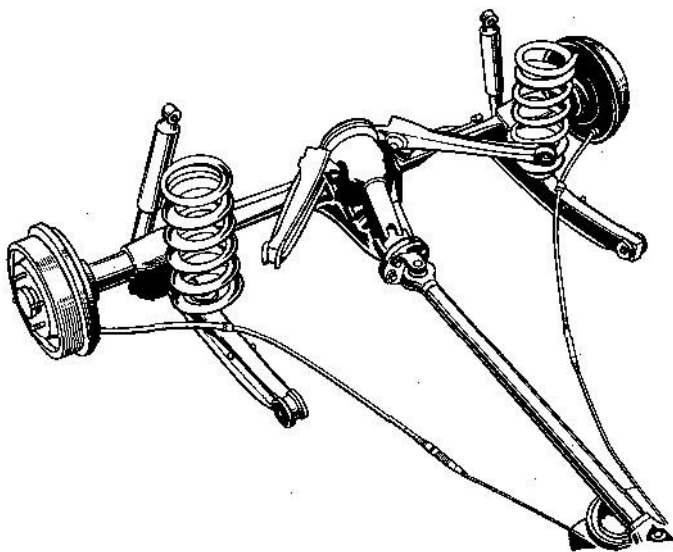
Задняя подвеска ведущих колес автомобиля «Форд-таунус» с косыми верхними рычагами. Пружины привернуты к нижним рычагам концами с уменьшенным диаметром навитки. Амортизаторы расположены позади оси колес
